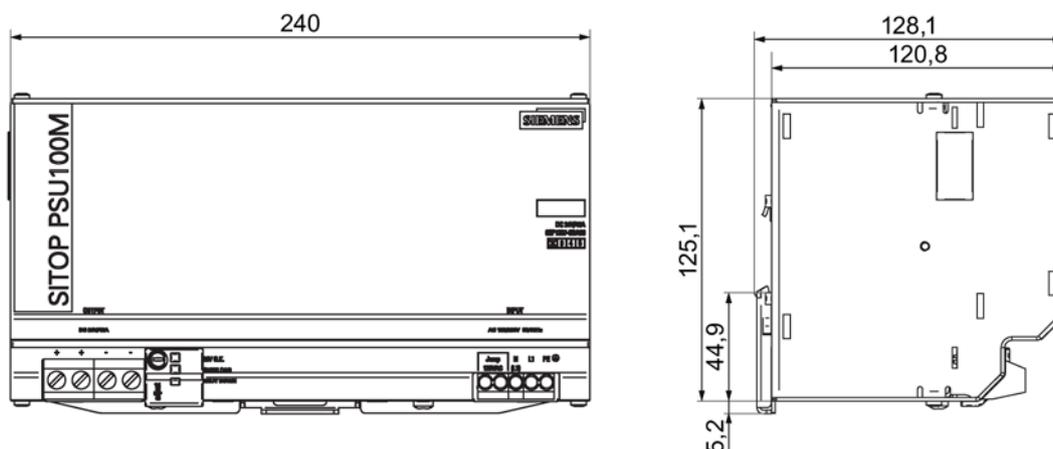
Maßzeichnung 6EP1337-3BA00
